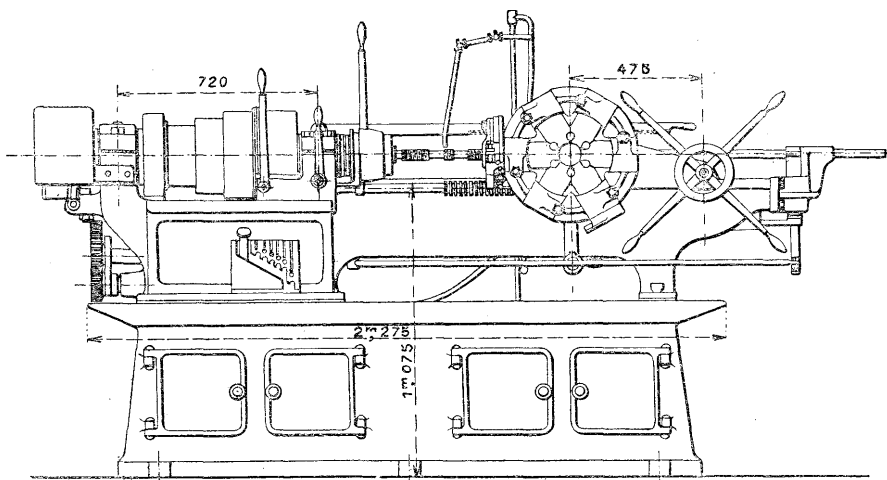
Tour de la Wolseley Sheep Shearing Company, de Birmingham. — Vue d'avant.
